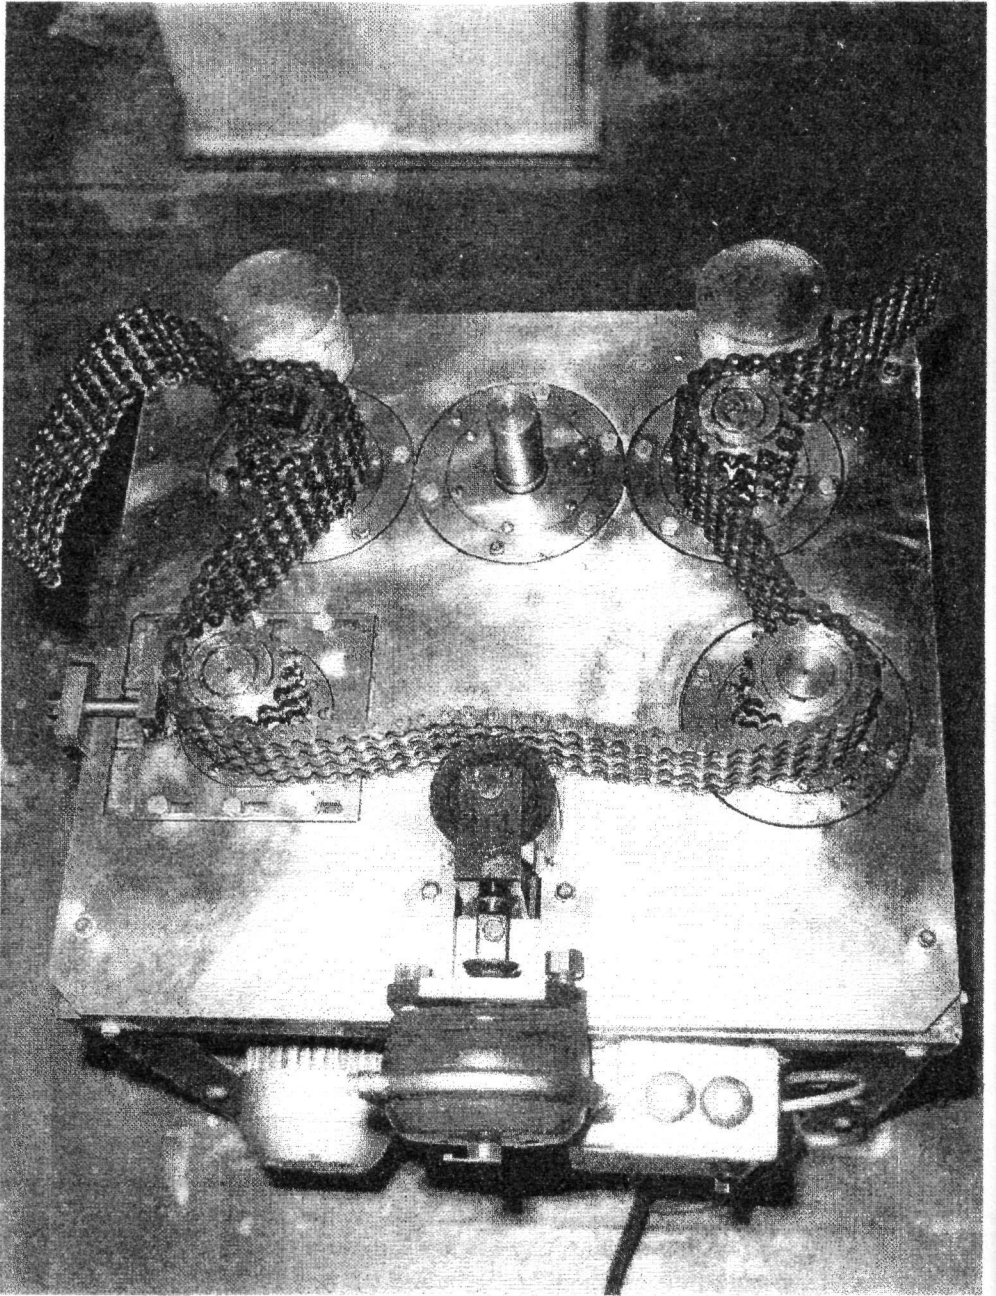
Загальний вигляд верстата для пластичного деформування приводних ланцюгів
